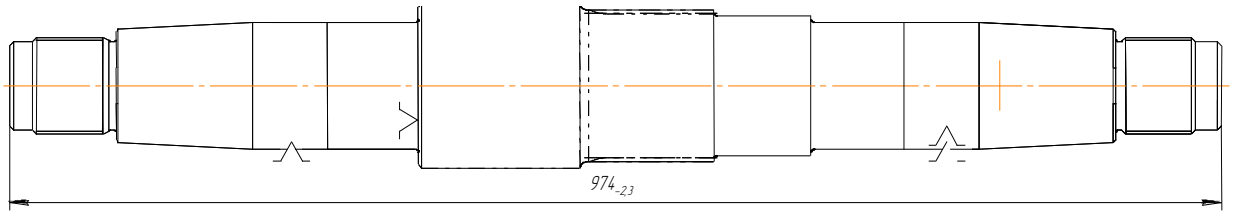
Теоретична схема базування на фрезерну операцію
